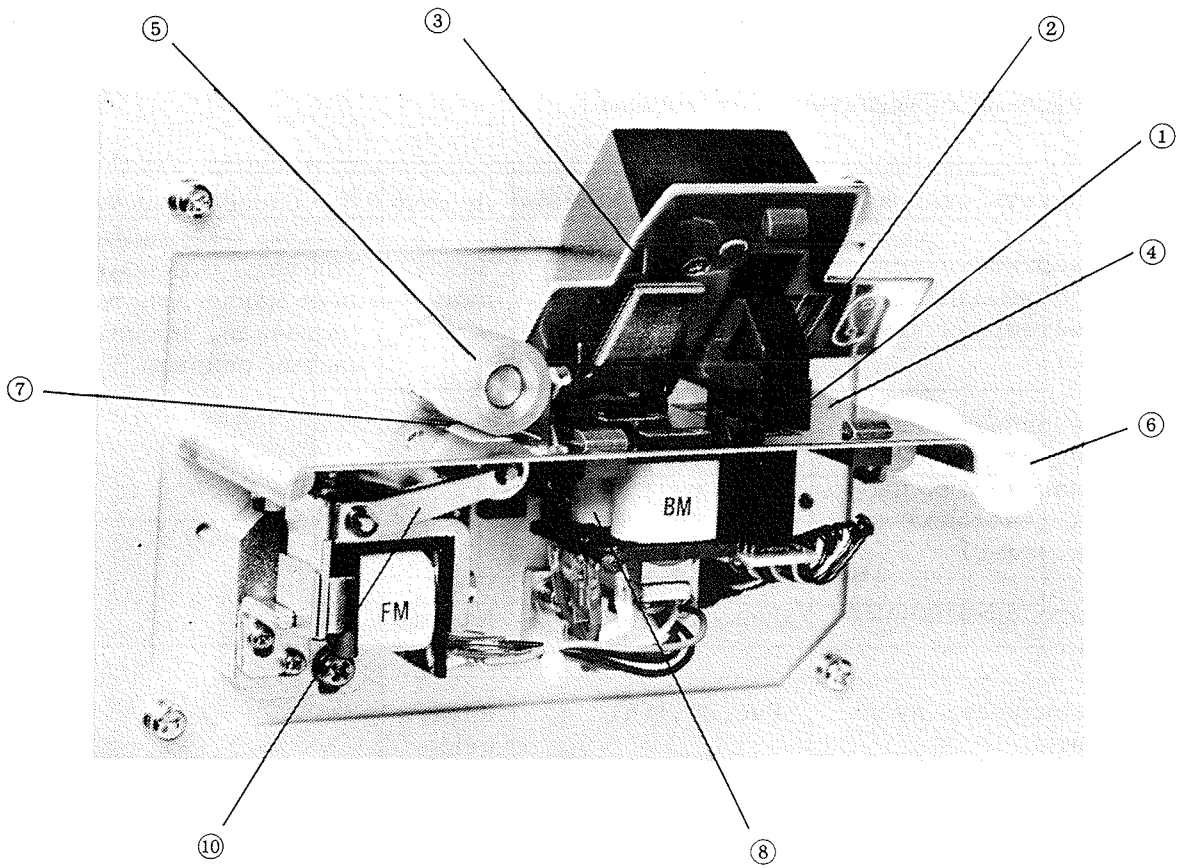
(а) Передний вид ленточного считывателя без бобины
